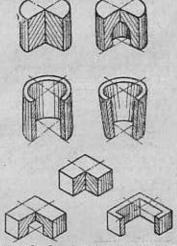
Заготовки для выдавливания мастер-пуансоном.
